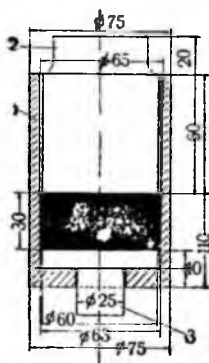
Приспособление Воронова для спрессовки баббитовой стружки:
